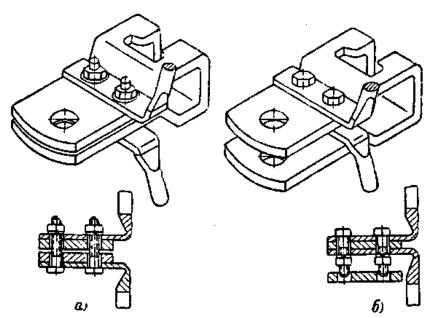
Крепления защитных колец на ушках изоляторов: a — крепление на онолапчатом ушке;  $\delta$  — крепление на двухлапчатом ушке
